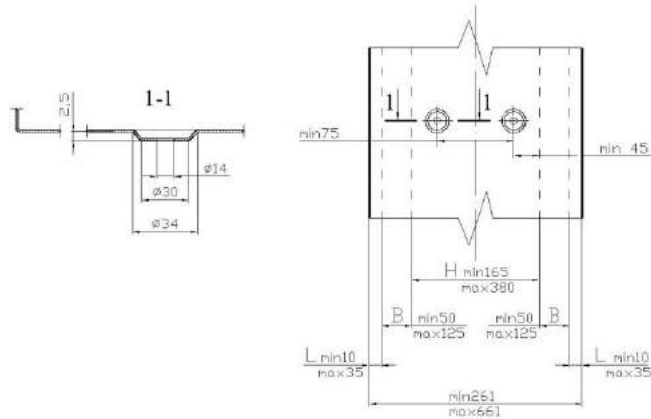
Схема расположения «пуклевки» в исходной заготовке профиля.
